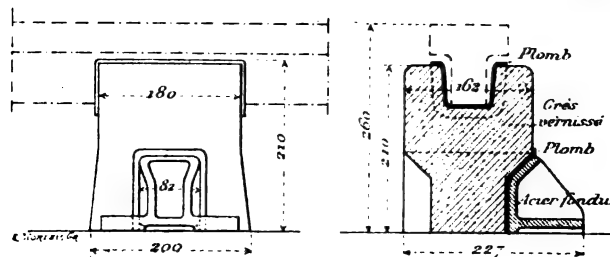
Isolateur en alignement droit. Vue latérale et coupe.
